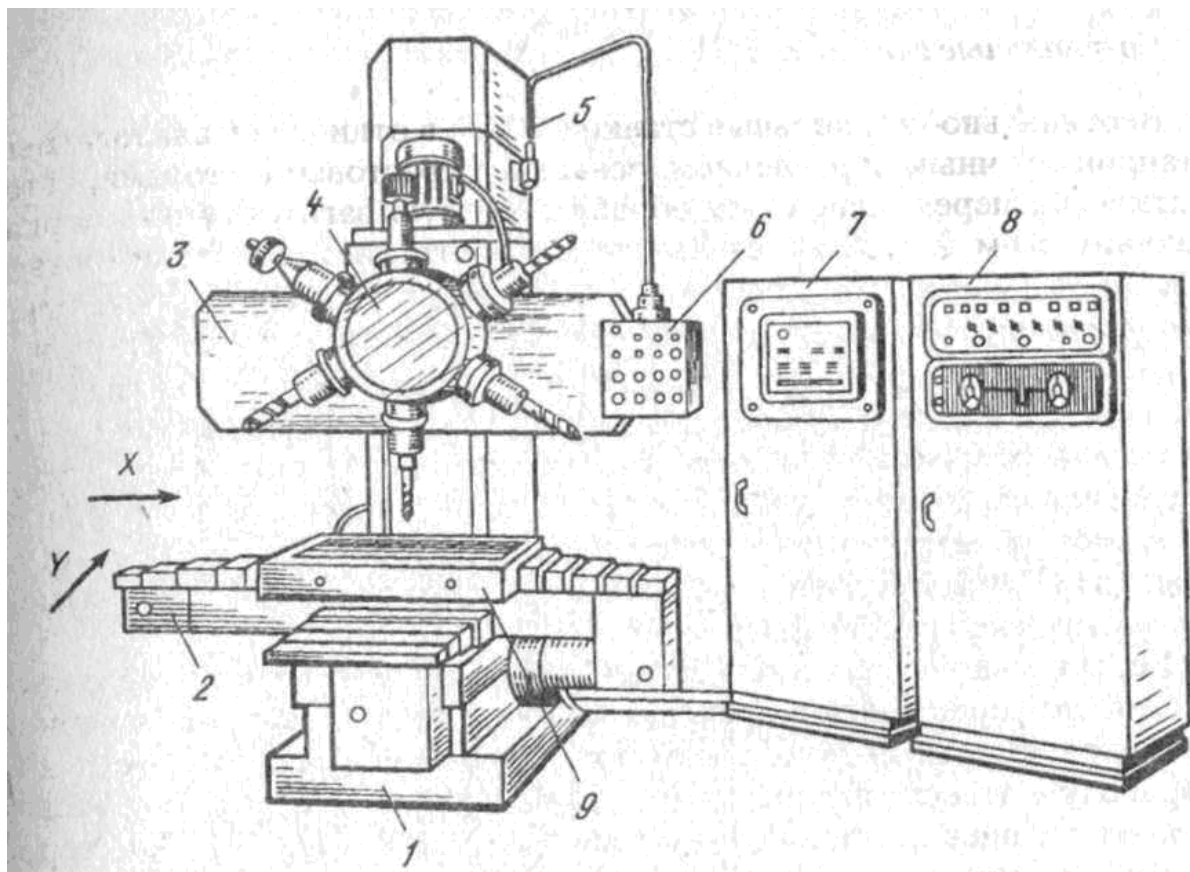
Вертикально-сверлильный станок модели 2P135Ф2-1.
